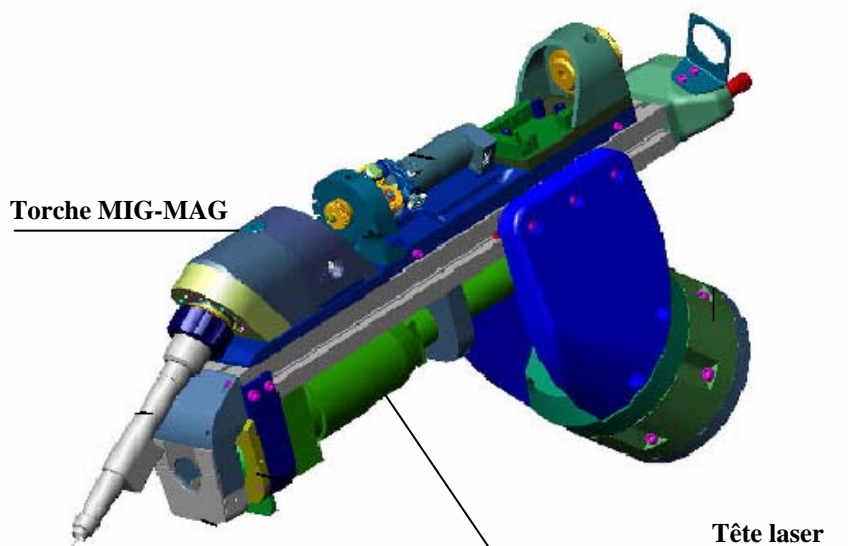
Principe d'une tête de soudage laser hybride
